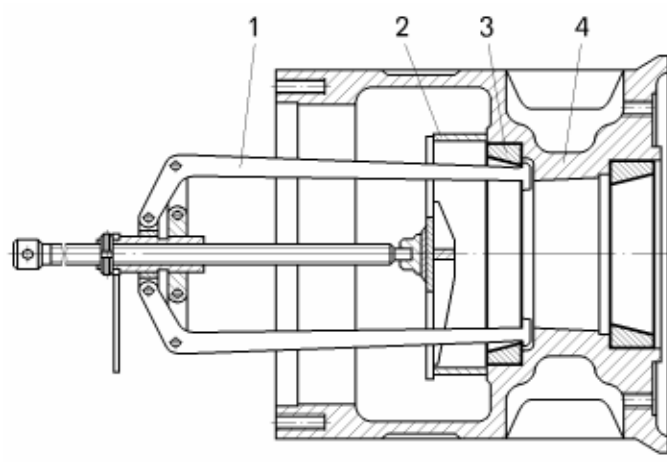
Выпрессовка наружных колец подшипников из ступицы колеса:
